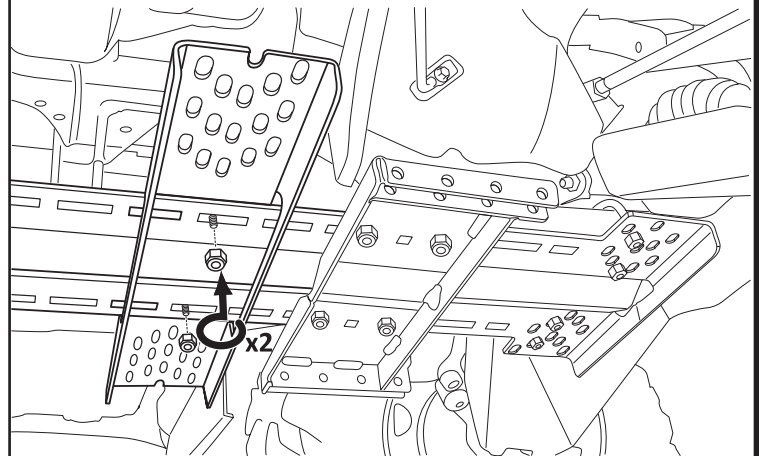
Hintere Kontaktplatte mit Gestellschrauben locker an der Mittelplatte befestigen.
